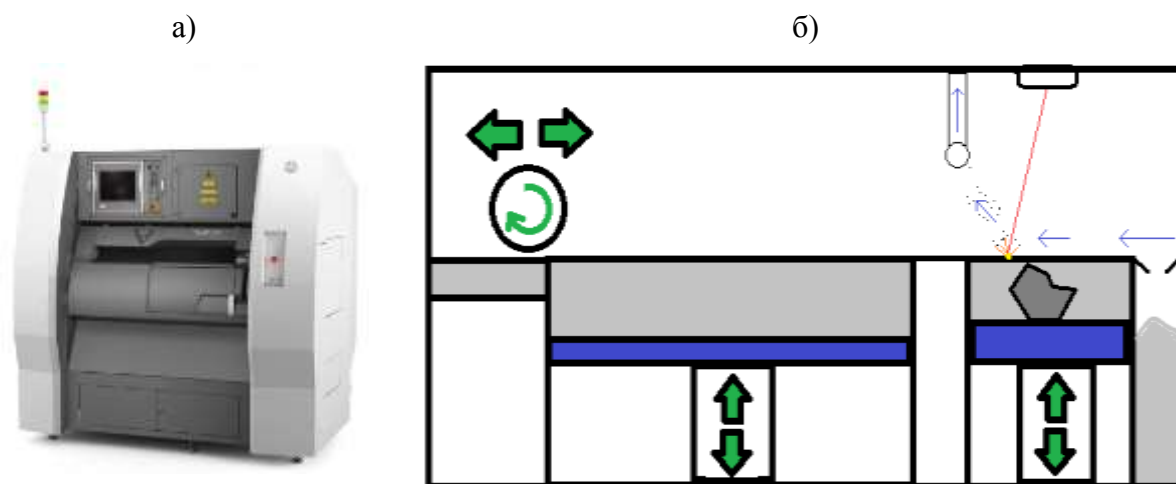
а – внешний вид установки ProX 300, б – схема рабочей камеры ProX 300
